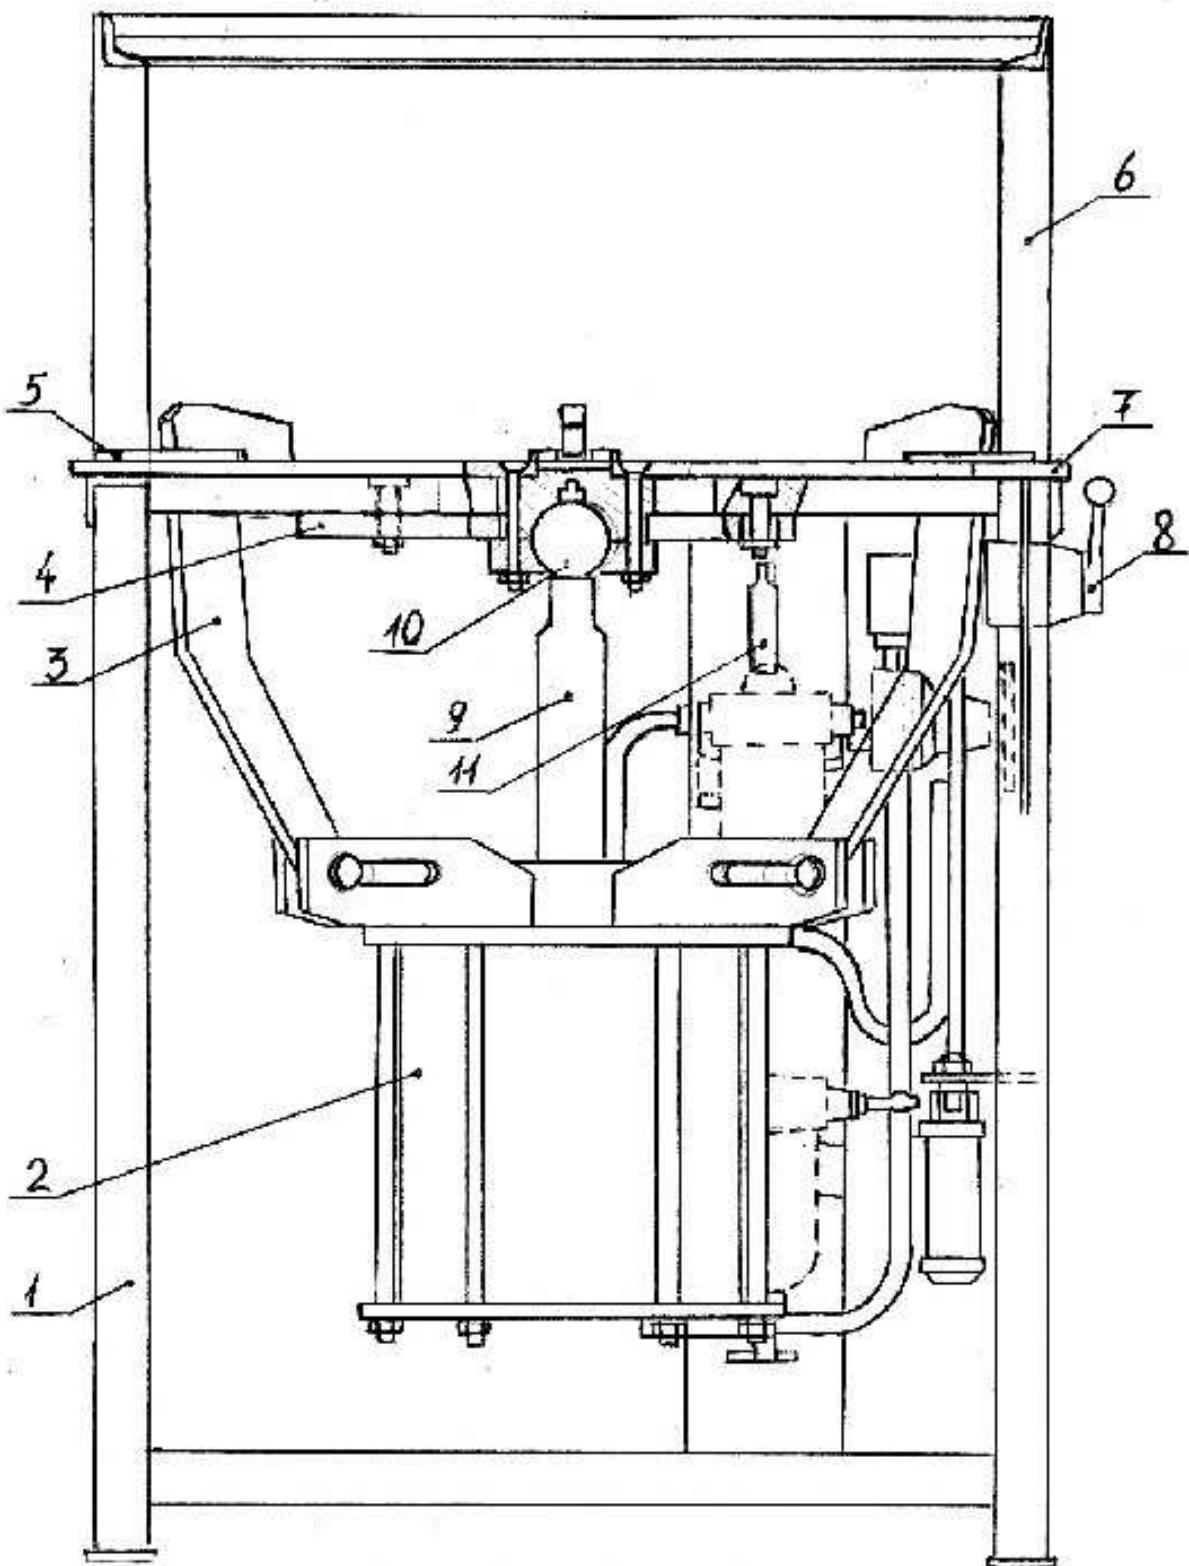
Столд для разборки (сборки) муфт сцепления.
